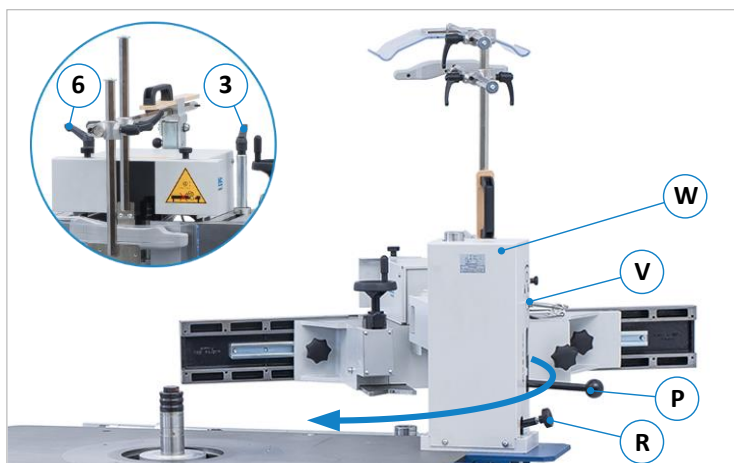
Hydraulische Wegschwenkvorrichtung
